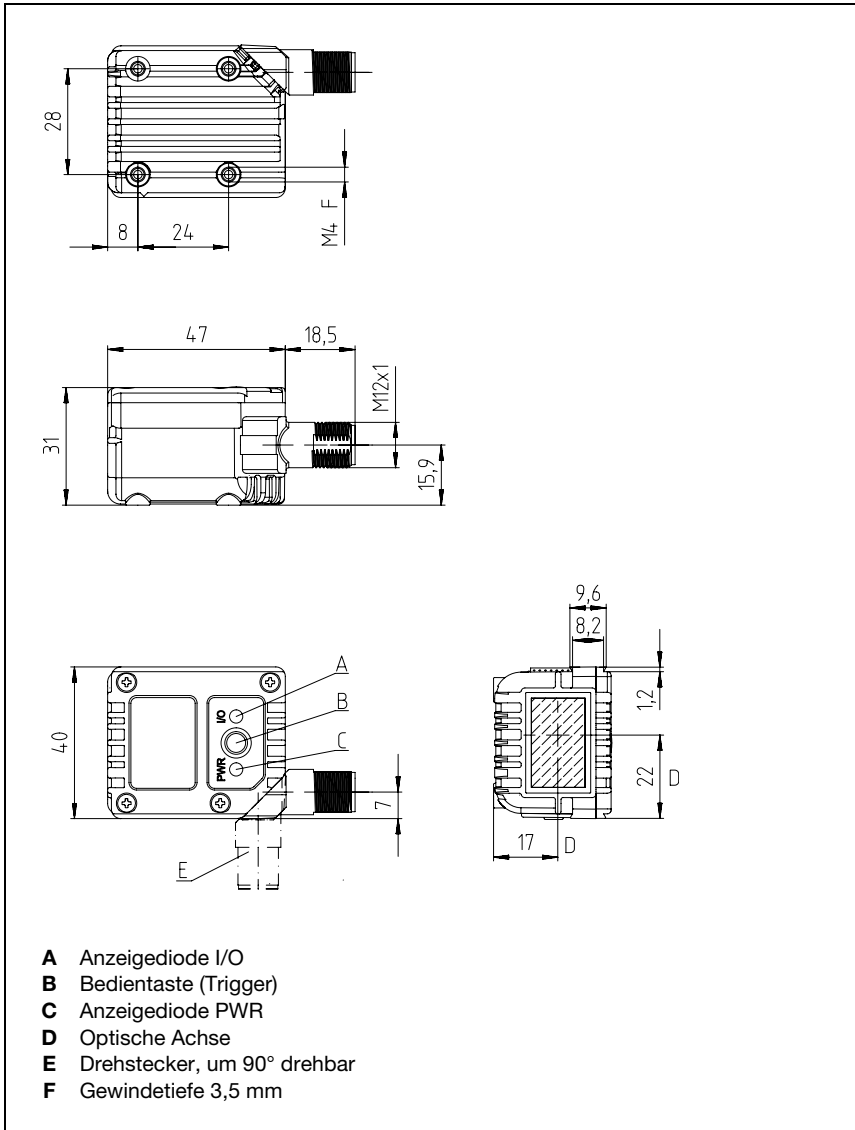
Maßzeichnung Codeleser LSIS 22x
